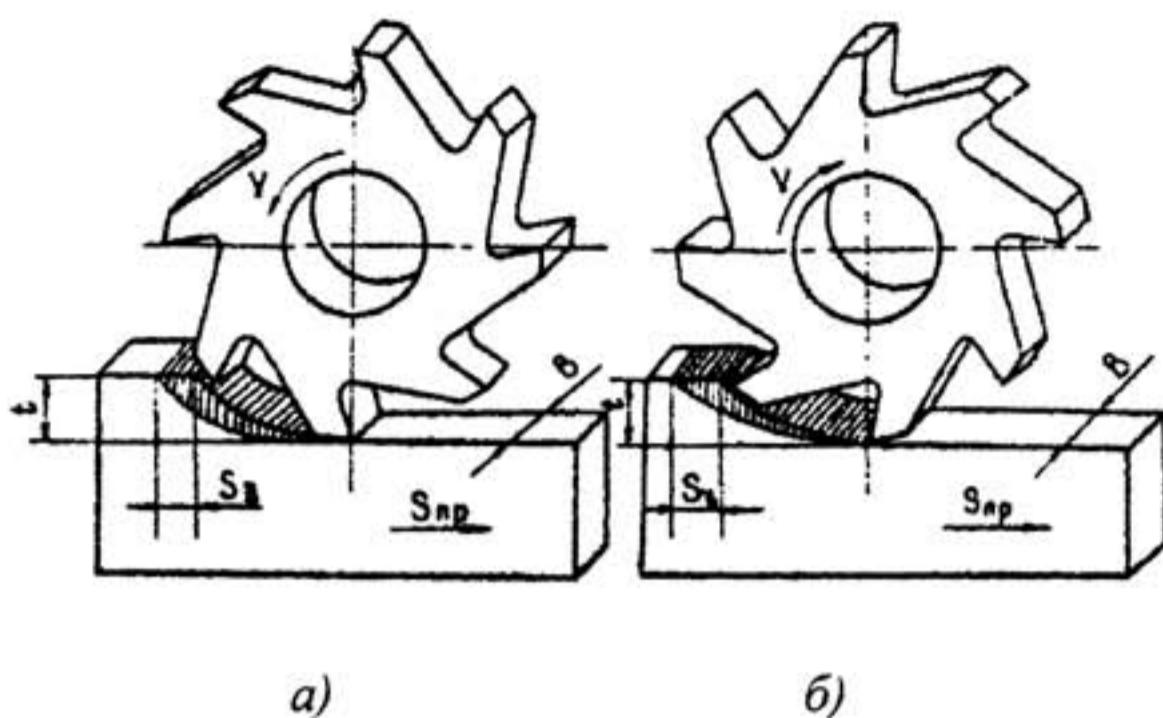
Схемы попутного (а) и встречного (б) фрезерования
